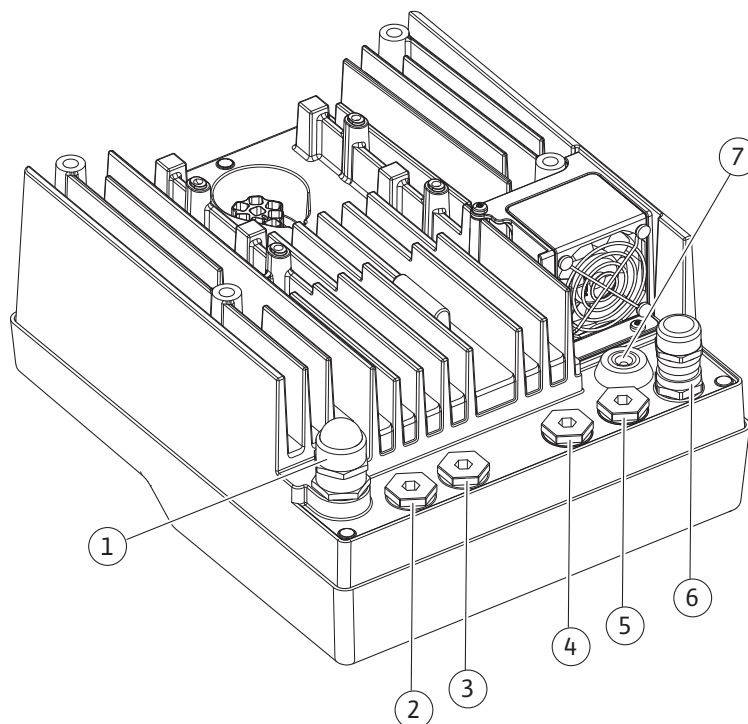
Presetupe pentru cablu/conexiuni de cablu
